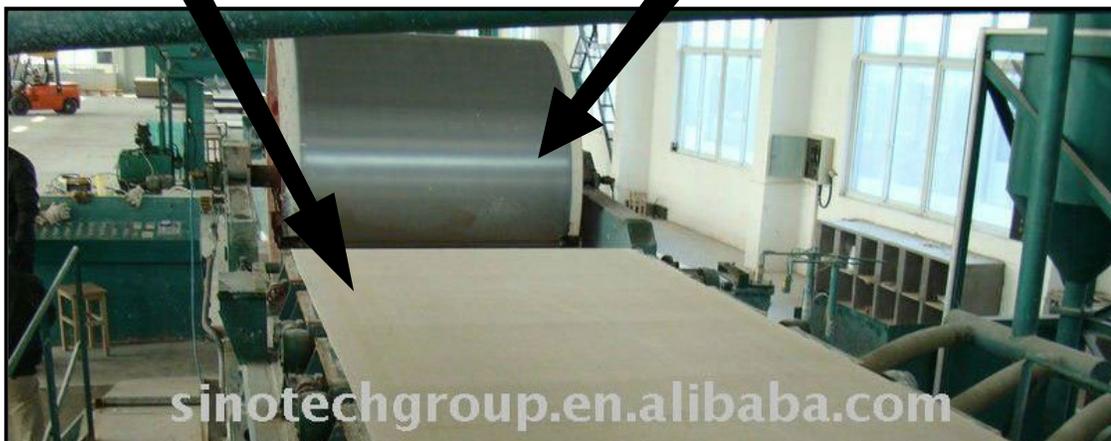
Fuente: Shanghai Sinotech Machinery Co.
